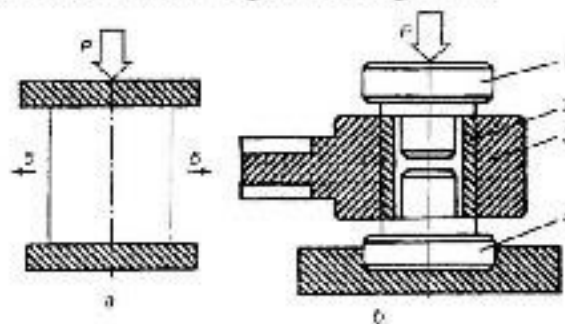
Пластическое деформирование осадкой: а — принципиальная схема метода; б — схема приспособления для осадки втулки; 1,4 — оправки; 2 — втулка; 3 — изделие
